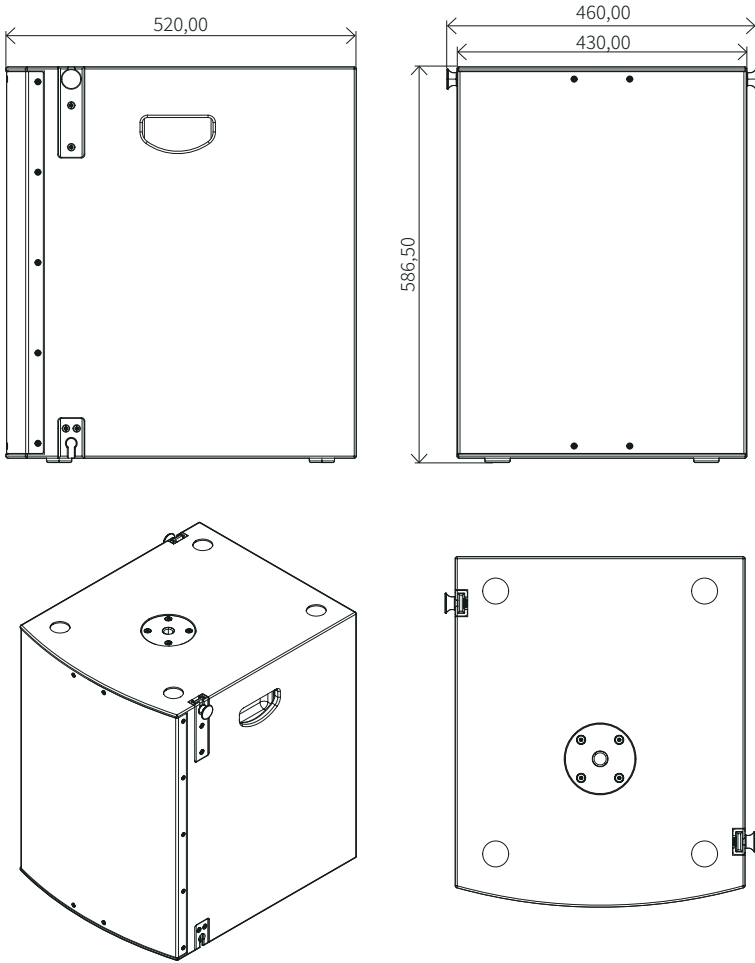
S15 PRO Ansichten und Abmessungen. Bemaßung in Millimetern.
